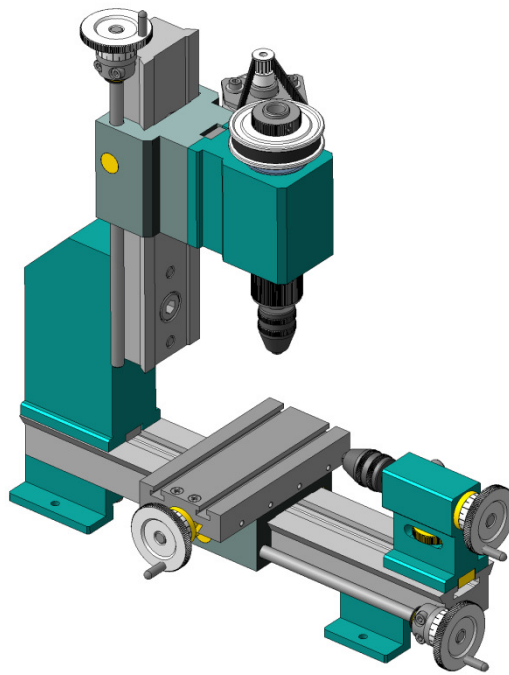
Модель компактного токарного верстата, який трансформований у в вертикально-фрезерний
